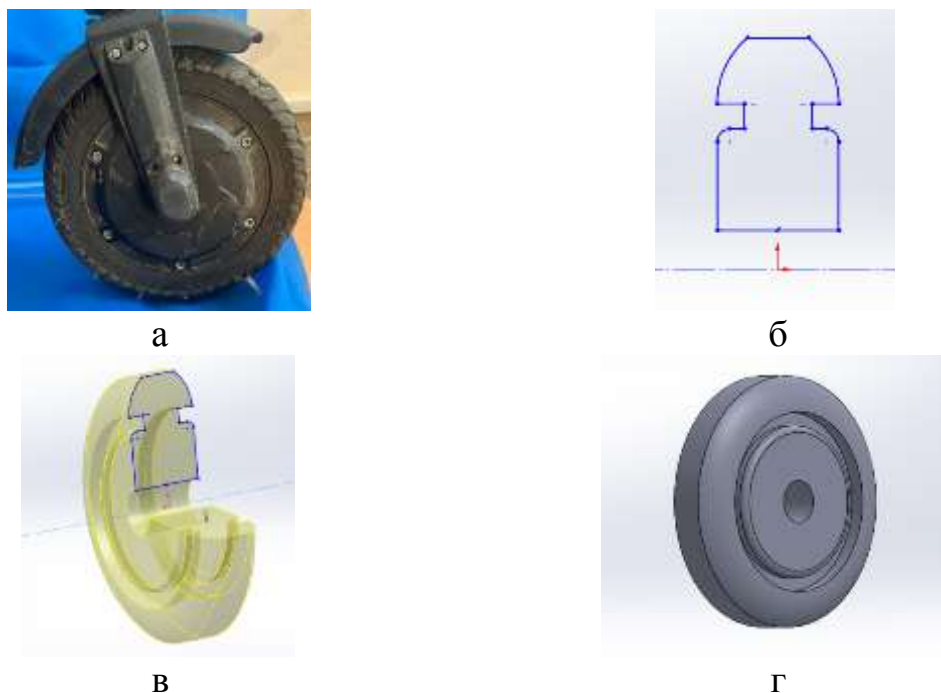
Ведущее колесо; а – реальный вид; б – эскиз среза мотор – колеса; в – команда «повернуть» эскиз; г – 3D-модель
